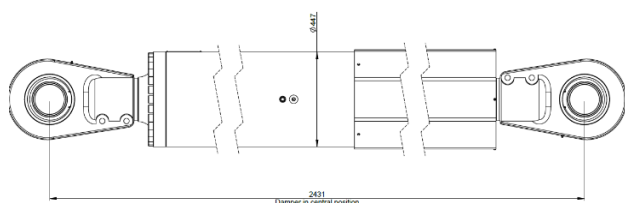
Vista longitudinal de un dispositivo MHD de amortiguación (Maurer)
